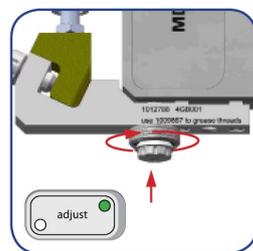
Adjust – Düsen-Einheit wieder reinschrauben
